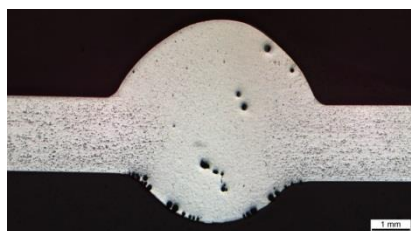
Микрошлиф сварного шва, $V = 4,5$ м/мин
